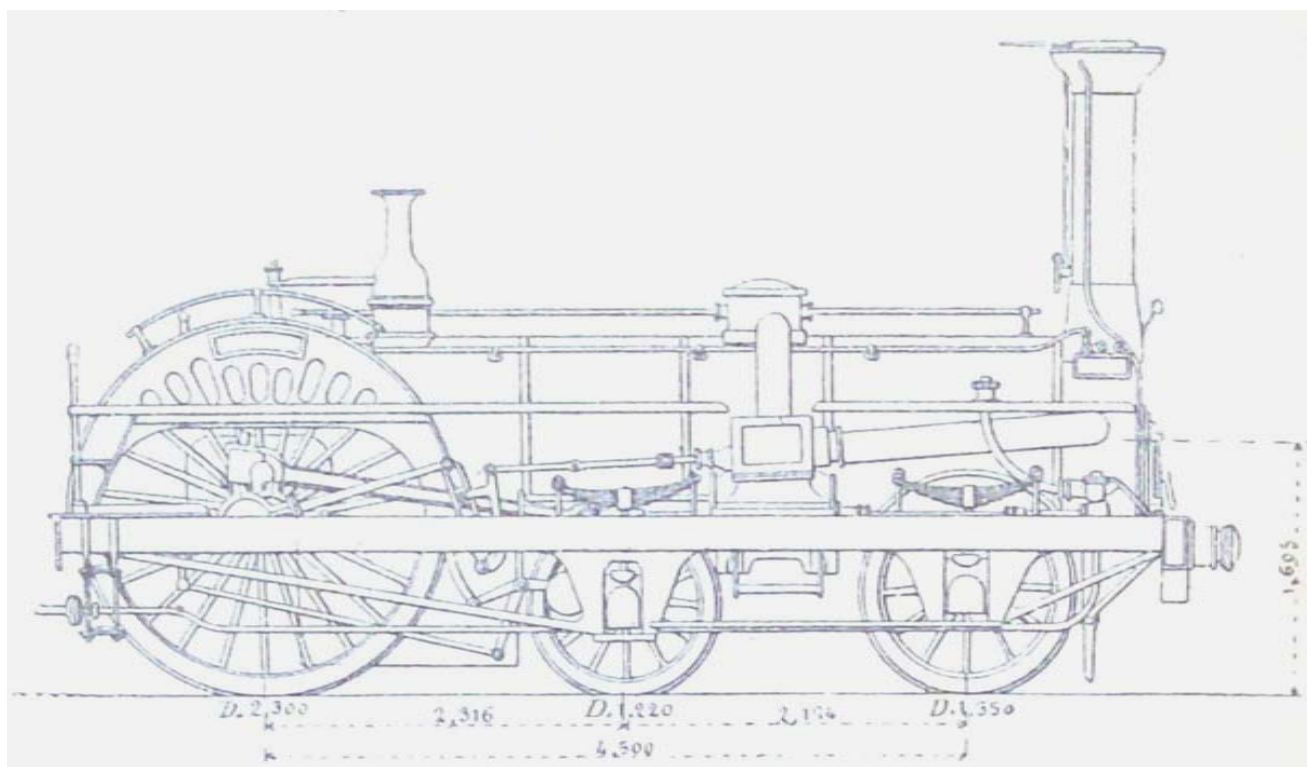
Locomotora Crampton del Est, s/ M.Demoulin
